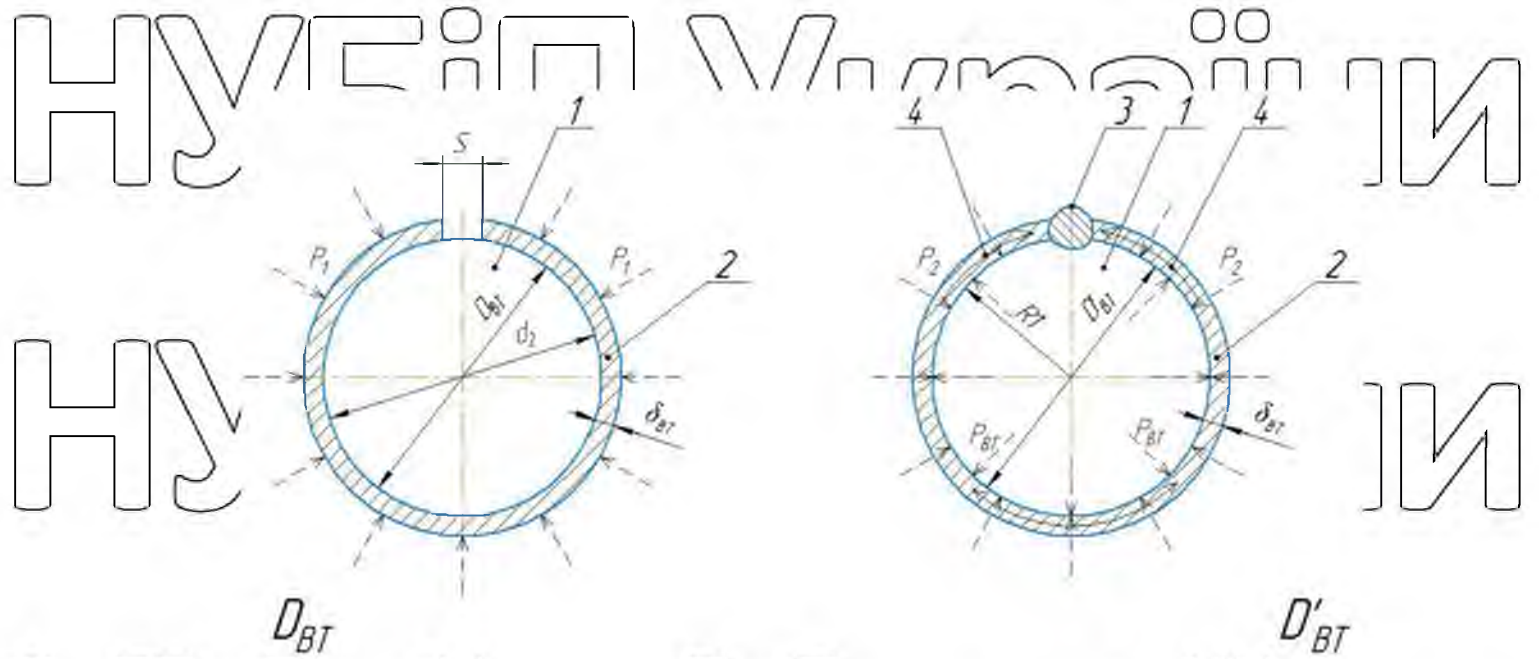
Схема установки загартованої розрізної ремонтної втулки на шийку валу:
